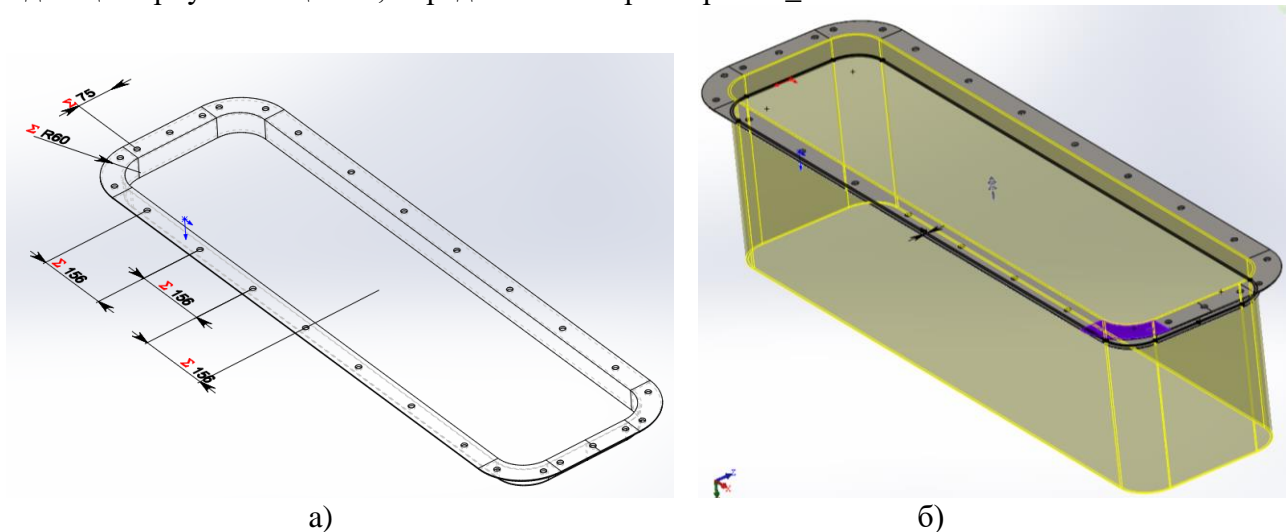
Построение фланцевой части (а) и боковых стенок (б) корпуса шнека
